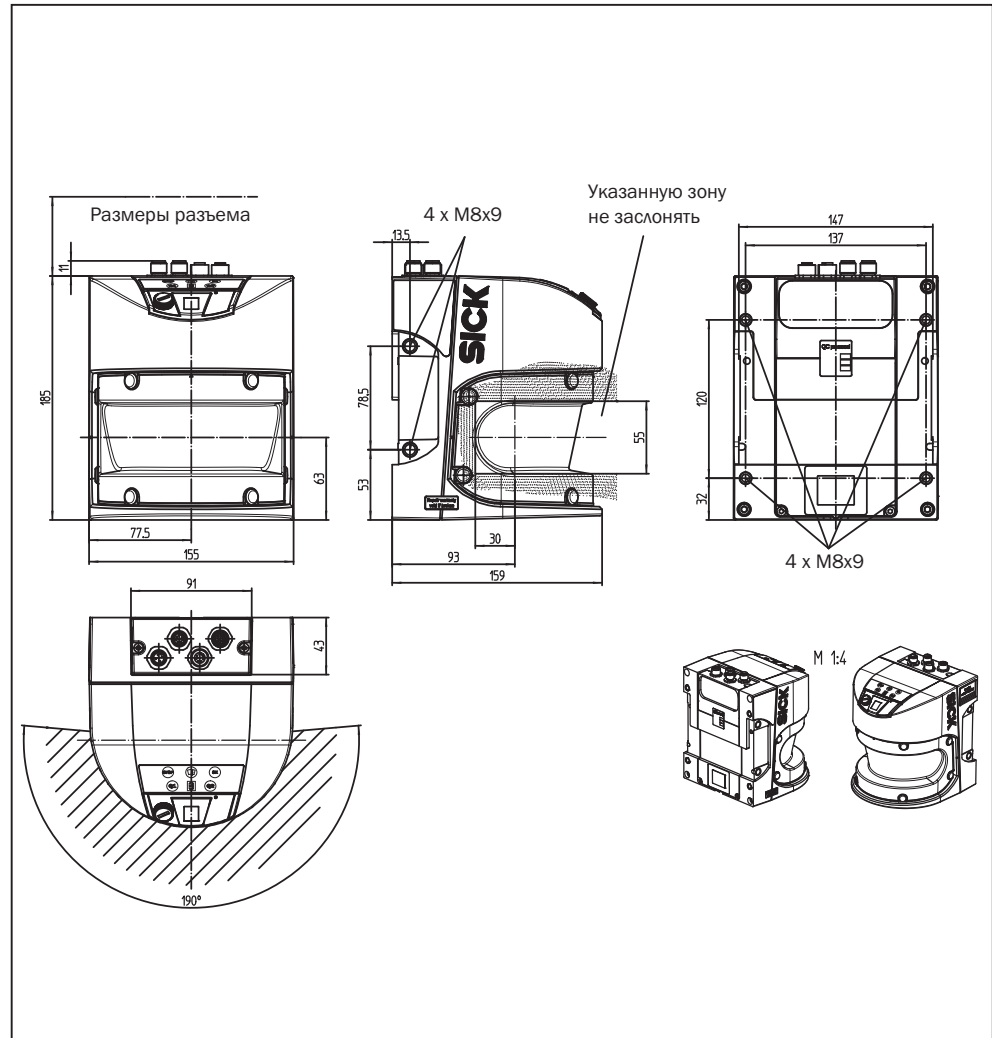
Размерный чертеж Bulkscan® LMS511 (мм)
